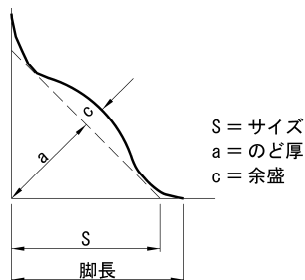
溶接のサイズ (道示Ⅱ編, 9.2.6)
